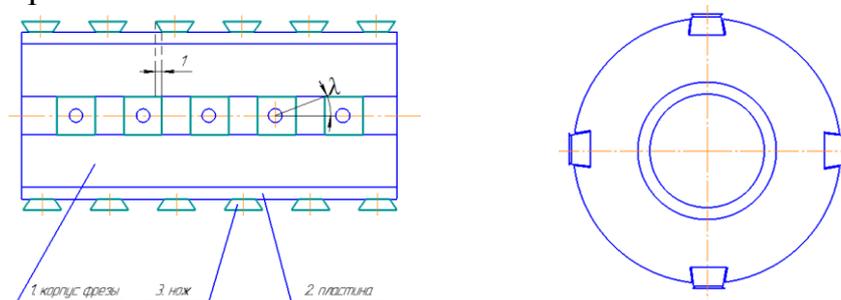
Фреза сборная с быстро заменяемыми ножами
